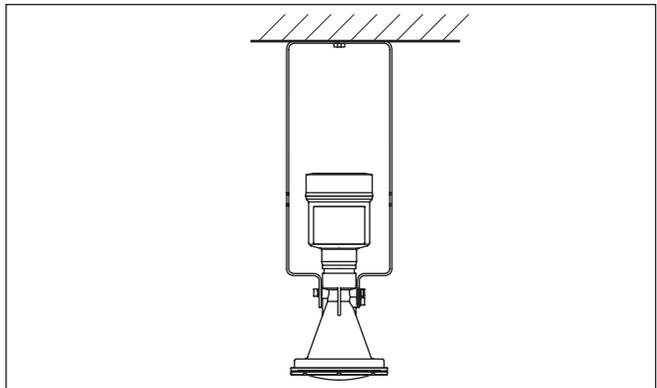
Montaje en el techo mediante el estribo de montaje con una longitud de 300 mm
